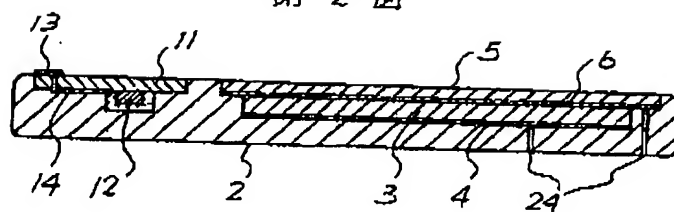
はIC基板、11は基板、12はICチップ、13は外部端子、2はカード基体、21はIC基板装着用凹部、3は表示片、4、8は接着剤層、5は透明保護シート、6は透明接着剤層、7は中間シートである。
